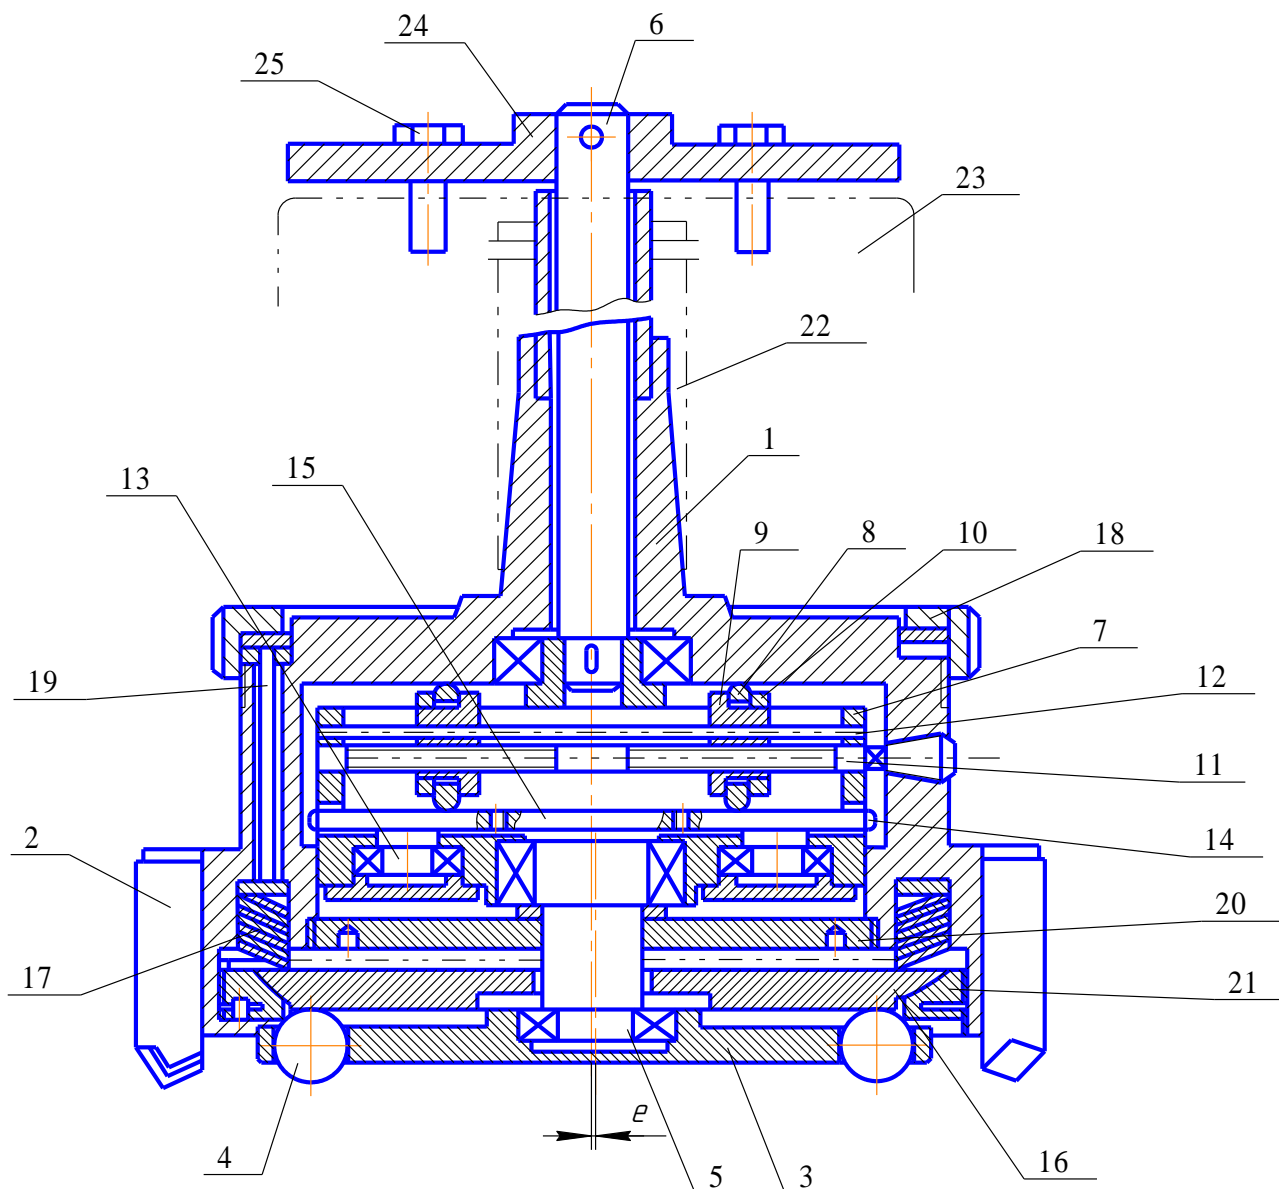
Пристрій для комбінованої обробки плоских поверхонь
